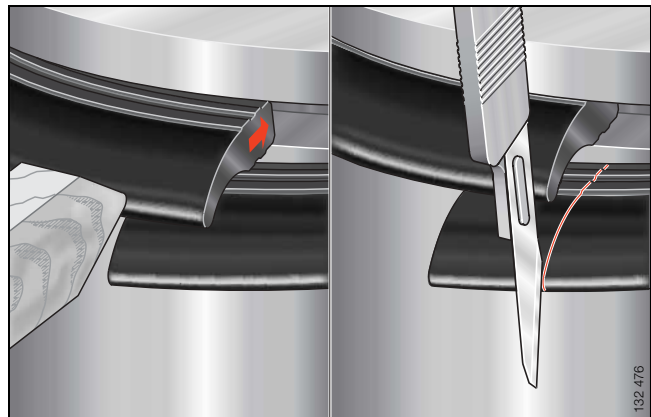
· Profil in Einbauraum drücken und zuschneiden
